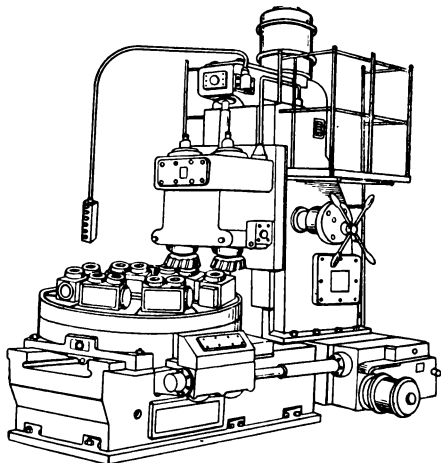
Двухшпindelный карусельно-фрезерный станок мод. 621
